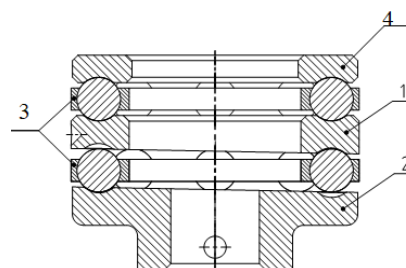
Подшипниковый узел головки: 1 – сменное кольцо; 2 – нижняя неподвижная втулка; 3 – сепараторы; 4 – верхнее кольцо
